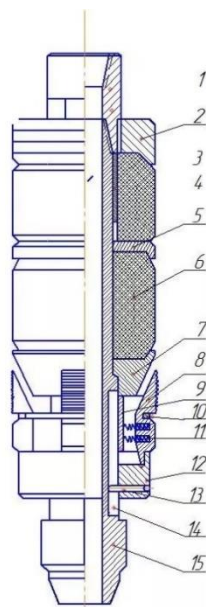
Вид механического пакера по типу ПВМ 122-500
